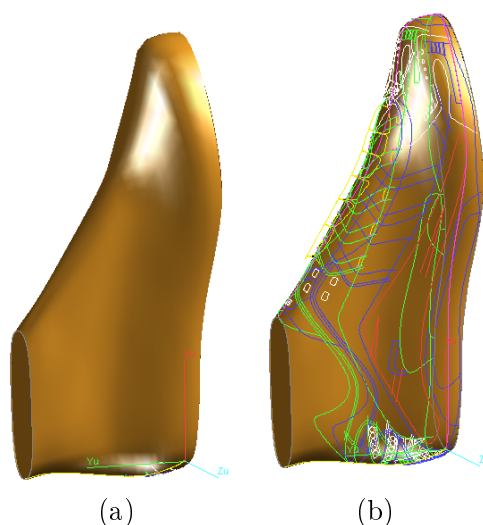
a) Chaussure 3D avec lignes de style cachées, b) Chaussure 3D avec lignes de style visibles.
